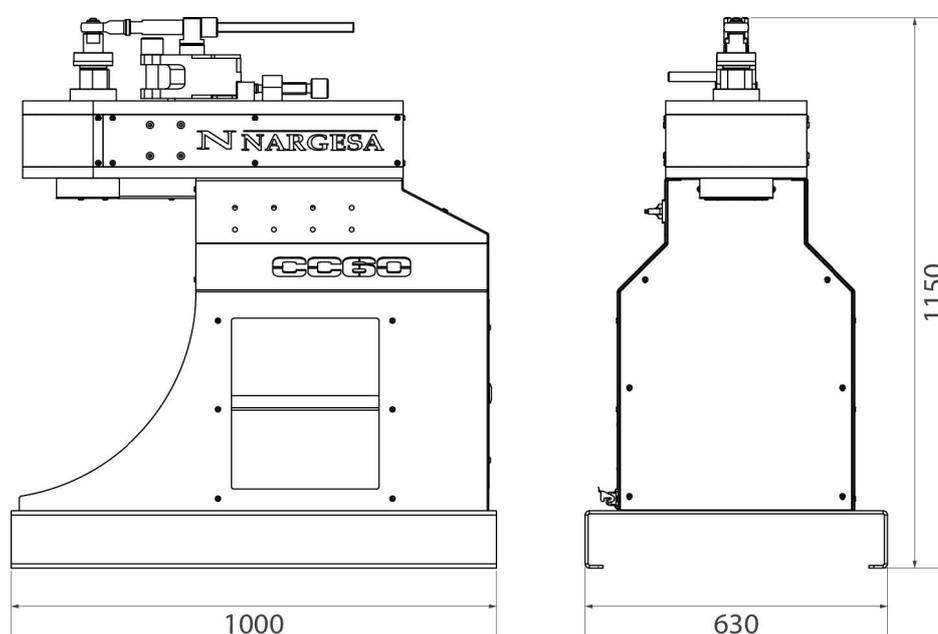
Dimensiones exteriores de la Curvadora CC60CNC
